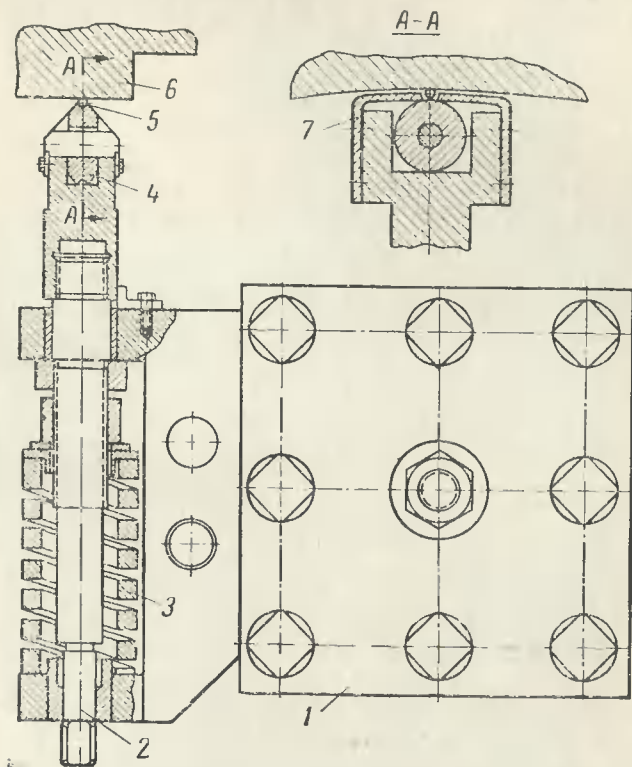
Приспособление для раскатывания расточки корпуса уплотнения.
